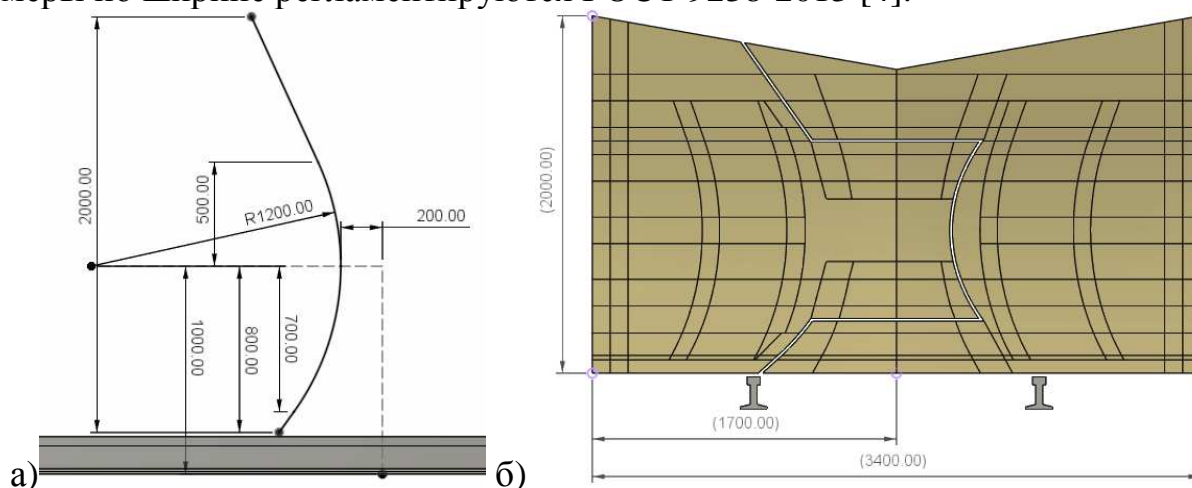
Форма щита отвала: а – профиль щита; б – габаритные размеры (вид спереди)
